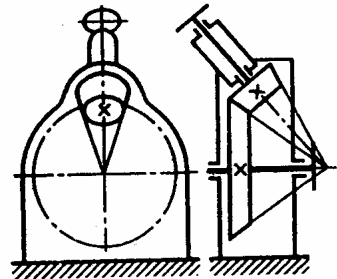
Кинематические схемы конических одноступенчатых редукторов.
